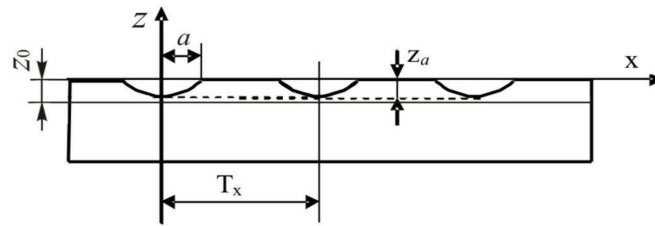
Канавки (криволинейные пазы) на поверхности заготовки
